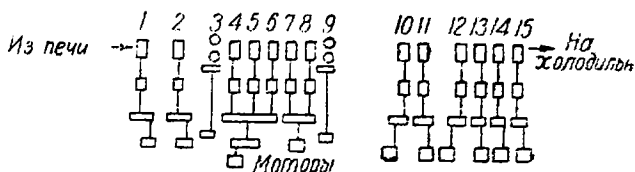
Непрерывно-заготовочный стан новых советских заводов
